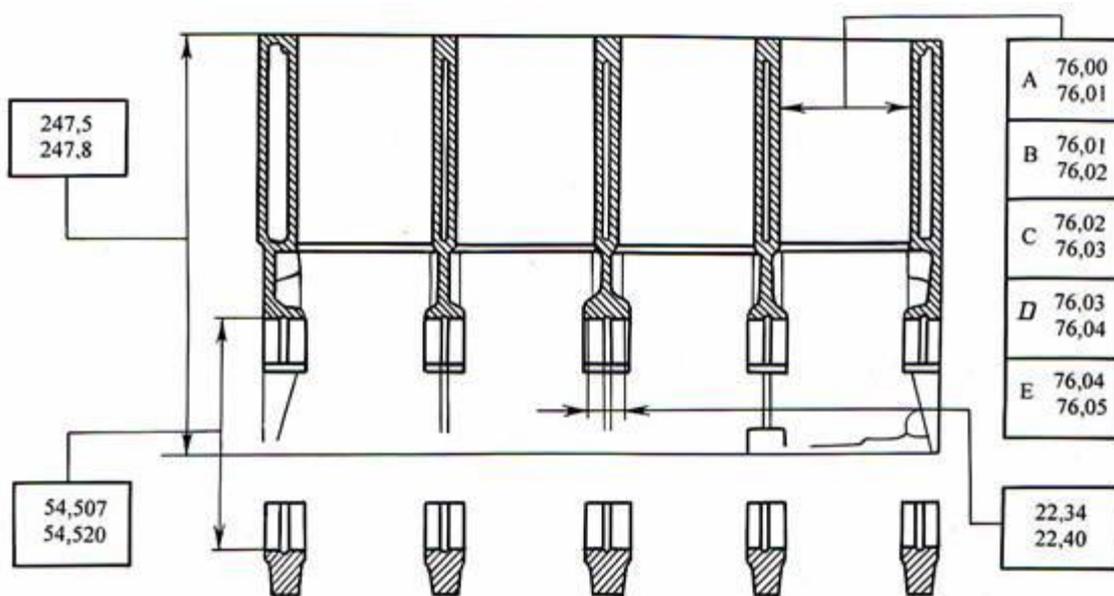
Контролируемые размеры блока цилиндров двигателя
